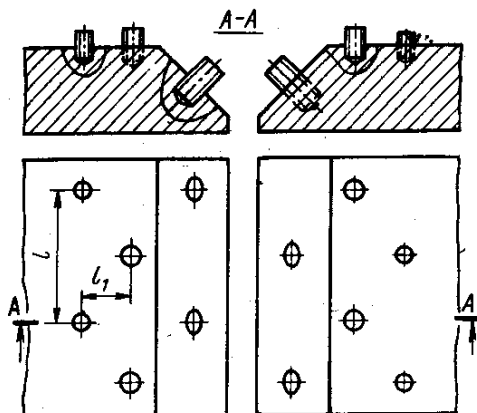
Подготовка чугунных деталей под сварку с помощью шпилек
